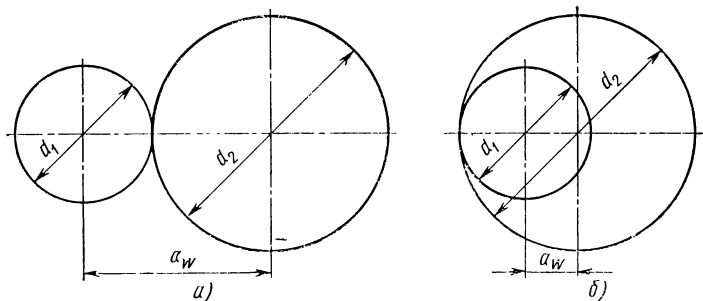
Цилиндрические зубчатые передачи внешнего (а) и внутреннего (б) зацепления
